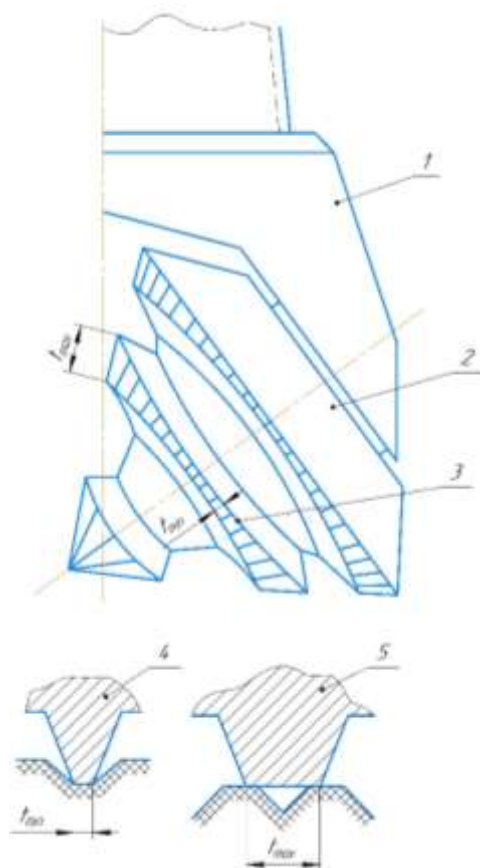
Долото с фрезерованными зубьями разной длины на венце шарошки.
